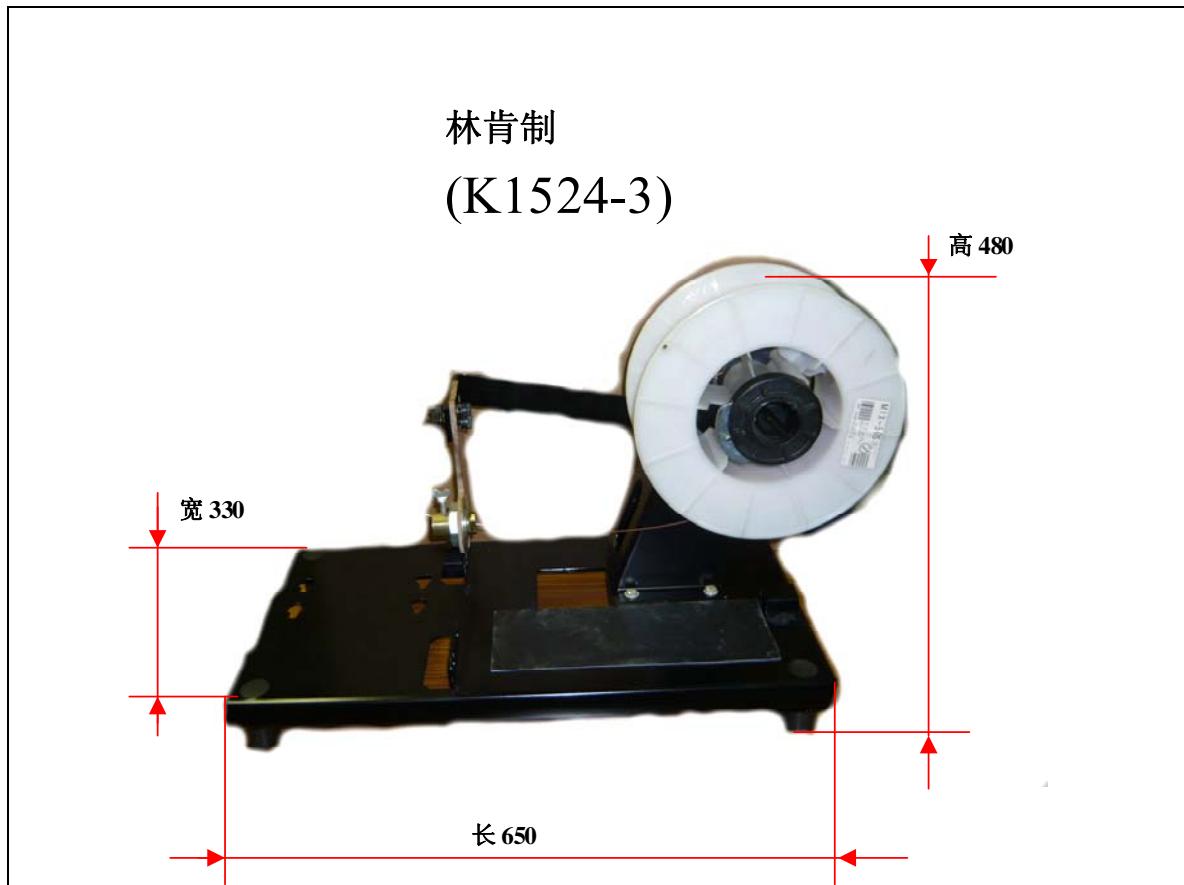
(f) 焊丝卷轴支架外形尺寸
